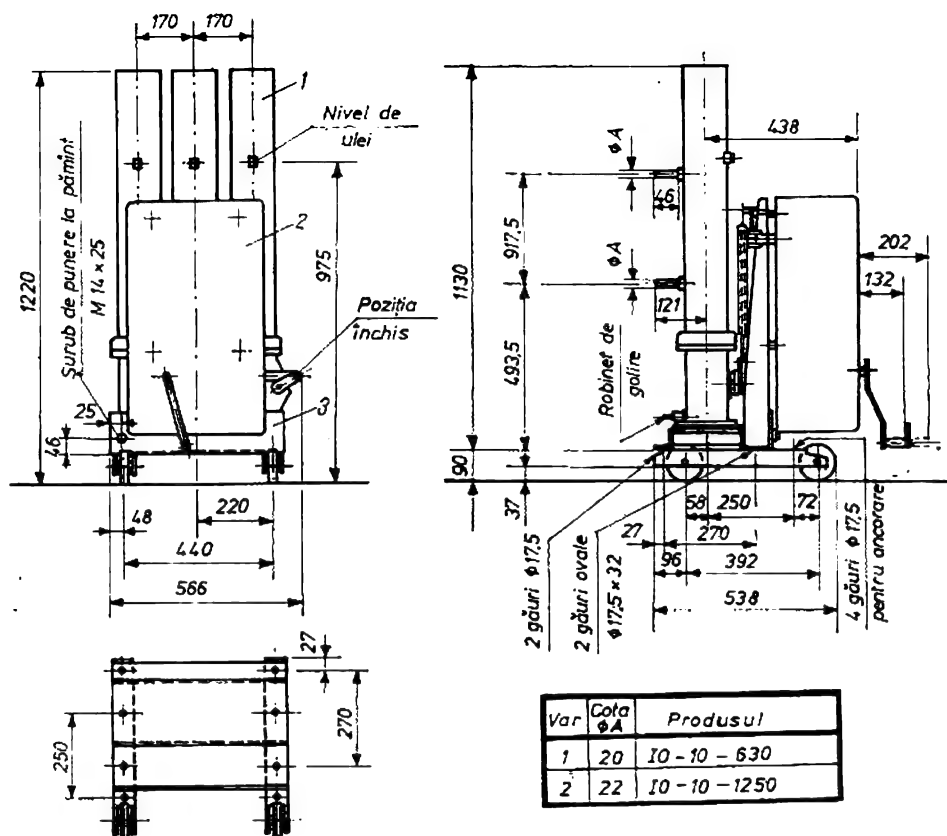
Înteruptoare IO-10/630, 1250. Dimensiuni de gabarit.
